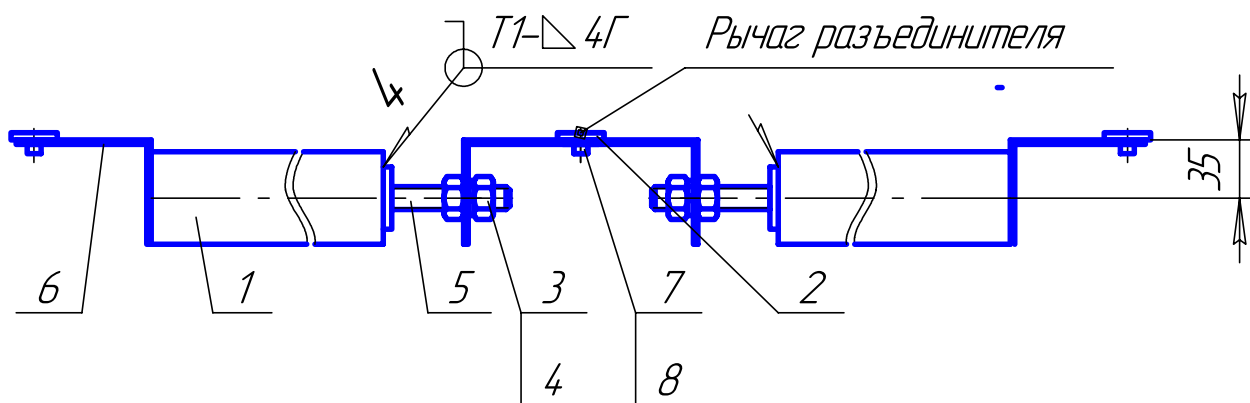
Установка соединительных тяг для управления главными ножами разъединителя.
